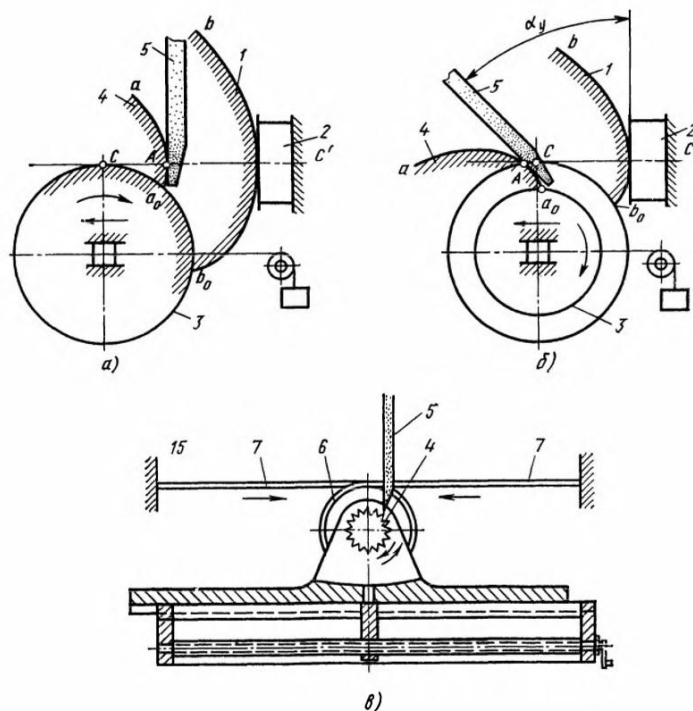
Шліфування евольвентної поверхні довбача плоскою стороною дискового круга при використанні механізмів: *а, б* – з евольвентним кулачком; на ніжці; *в* – з барабаном та сталевими стрічками:
